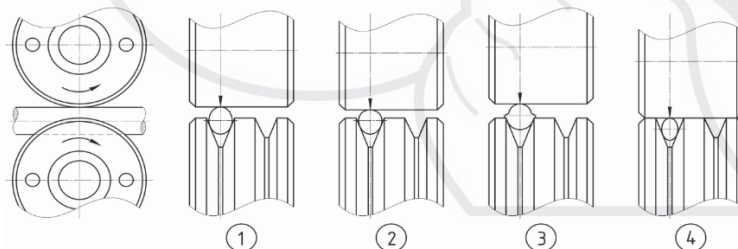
Усилие зажатия сварочной проволоки.
